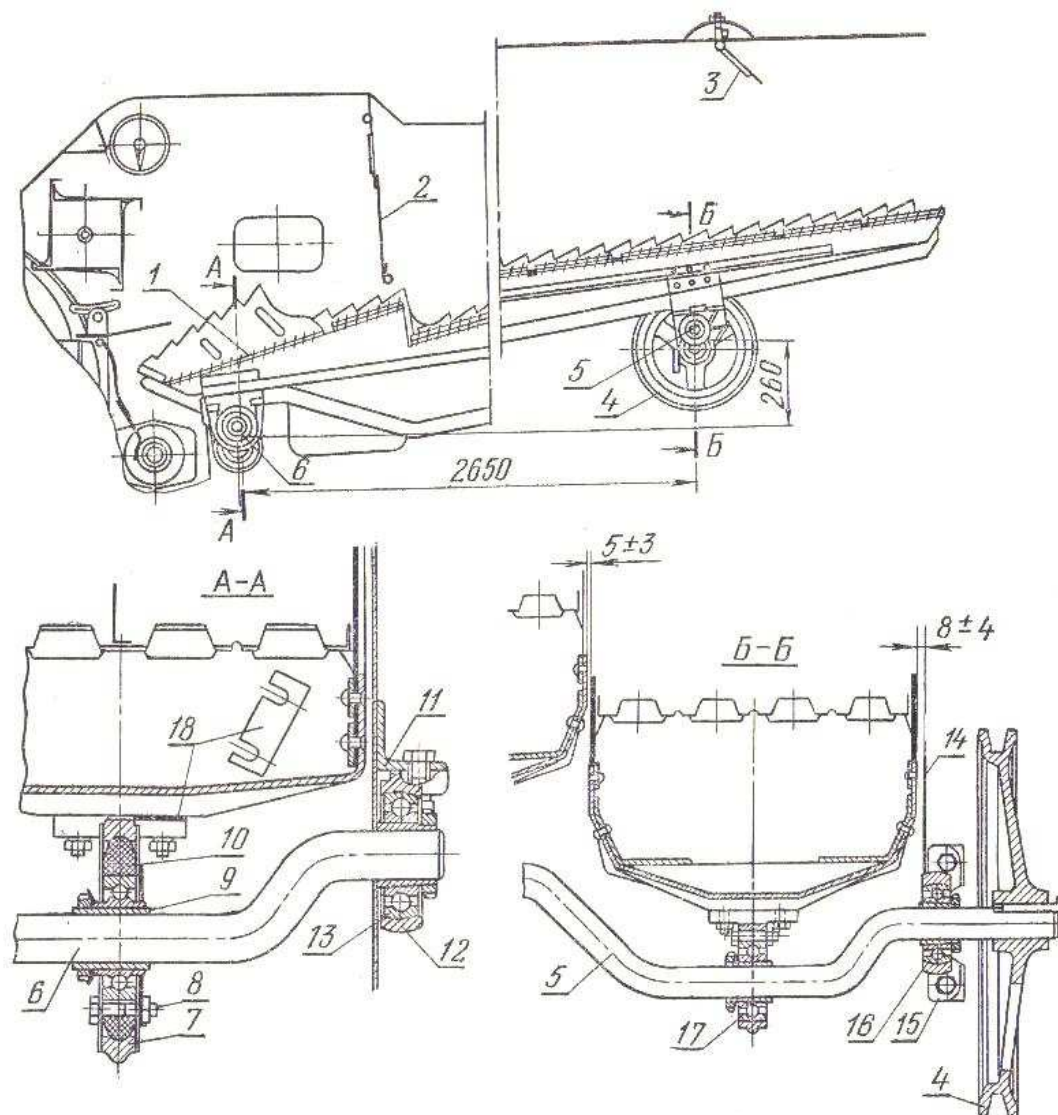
Сол омотряс комбайна СК-6: 1 – клавиша; 2 – клапан; 3 – клапан сигнального устройства; 4 – приводной шкив; 5 – задний коленчатый вал; 6 – передний коленчатый вал; 7, 12, 15 – корпуса подшипников; 8 – стяжной болт; 9 – втулка; 10 – сайленд-блок; 11 – кронштейн; 13, 16 – коренные подшипники; 14 – панель корпуса молотилки; 17 – опорный подшипник клавиши; 18 – прокладка
